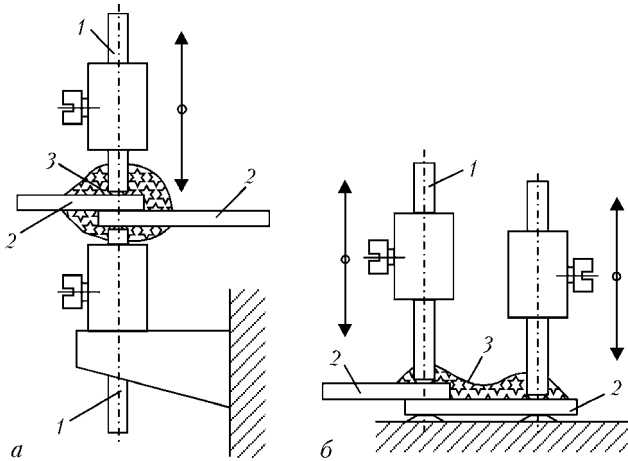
Схема газовой защиты при контактной сварке с двух- (а) и односторонним (б) расположением электродов: 1 — электроды; 2 — свариваемые детали; 3 — газоносная прослойка
